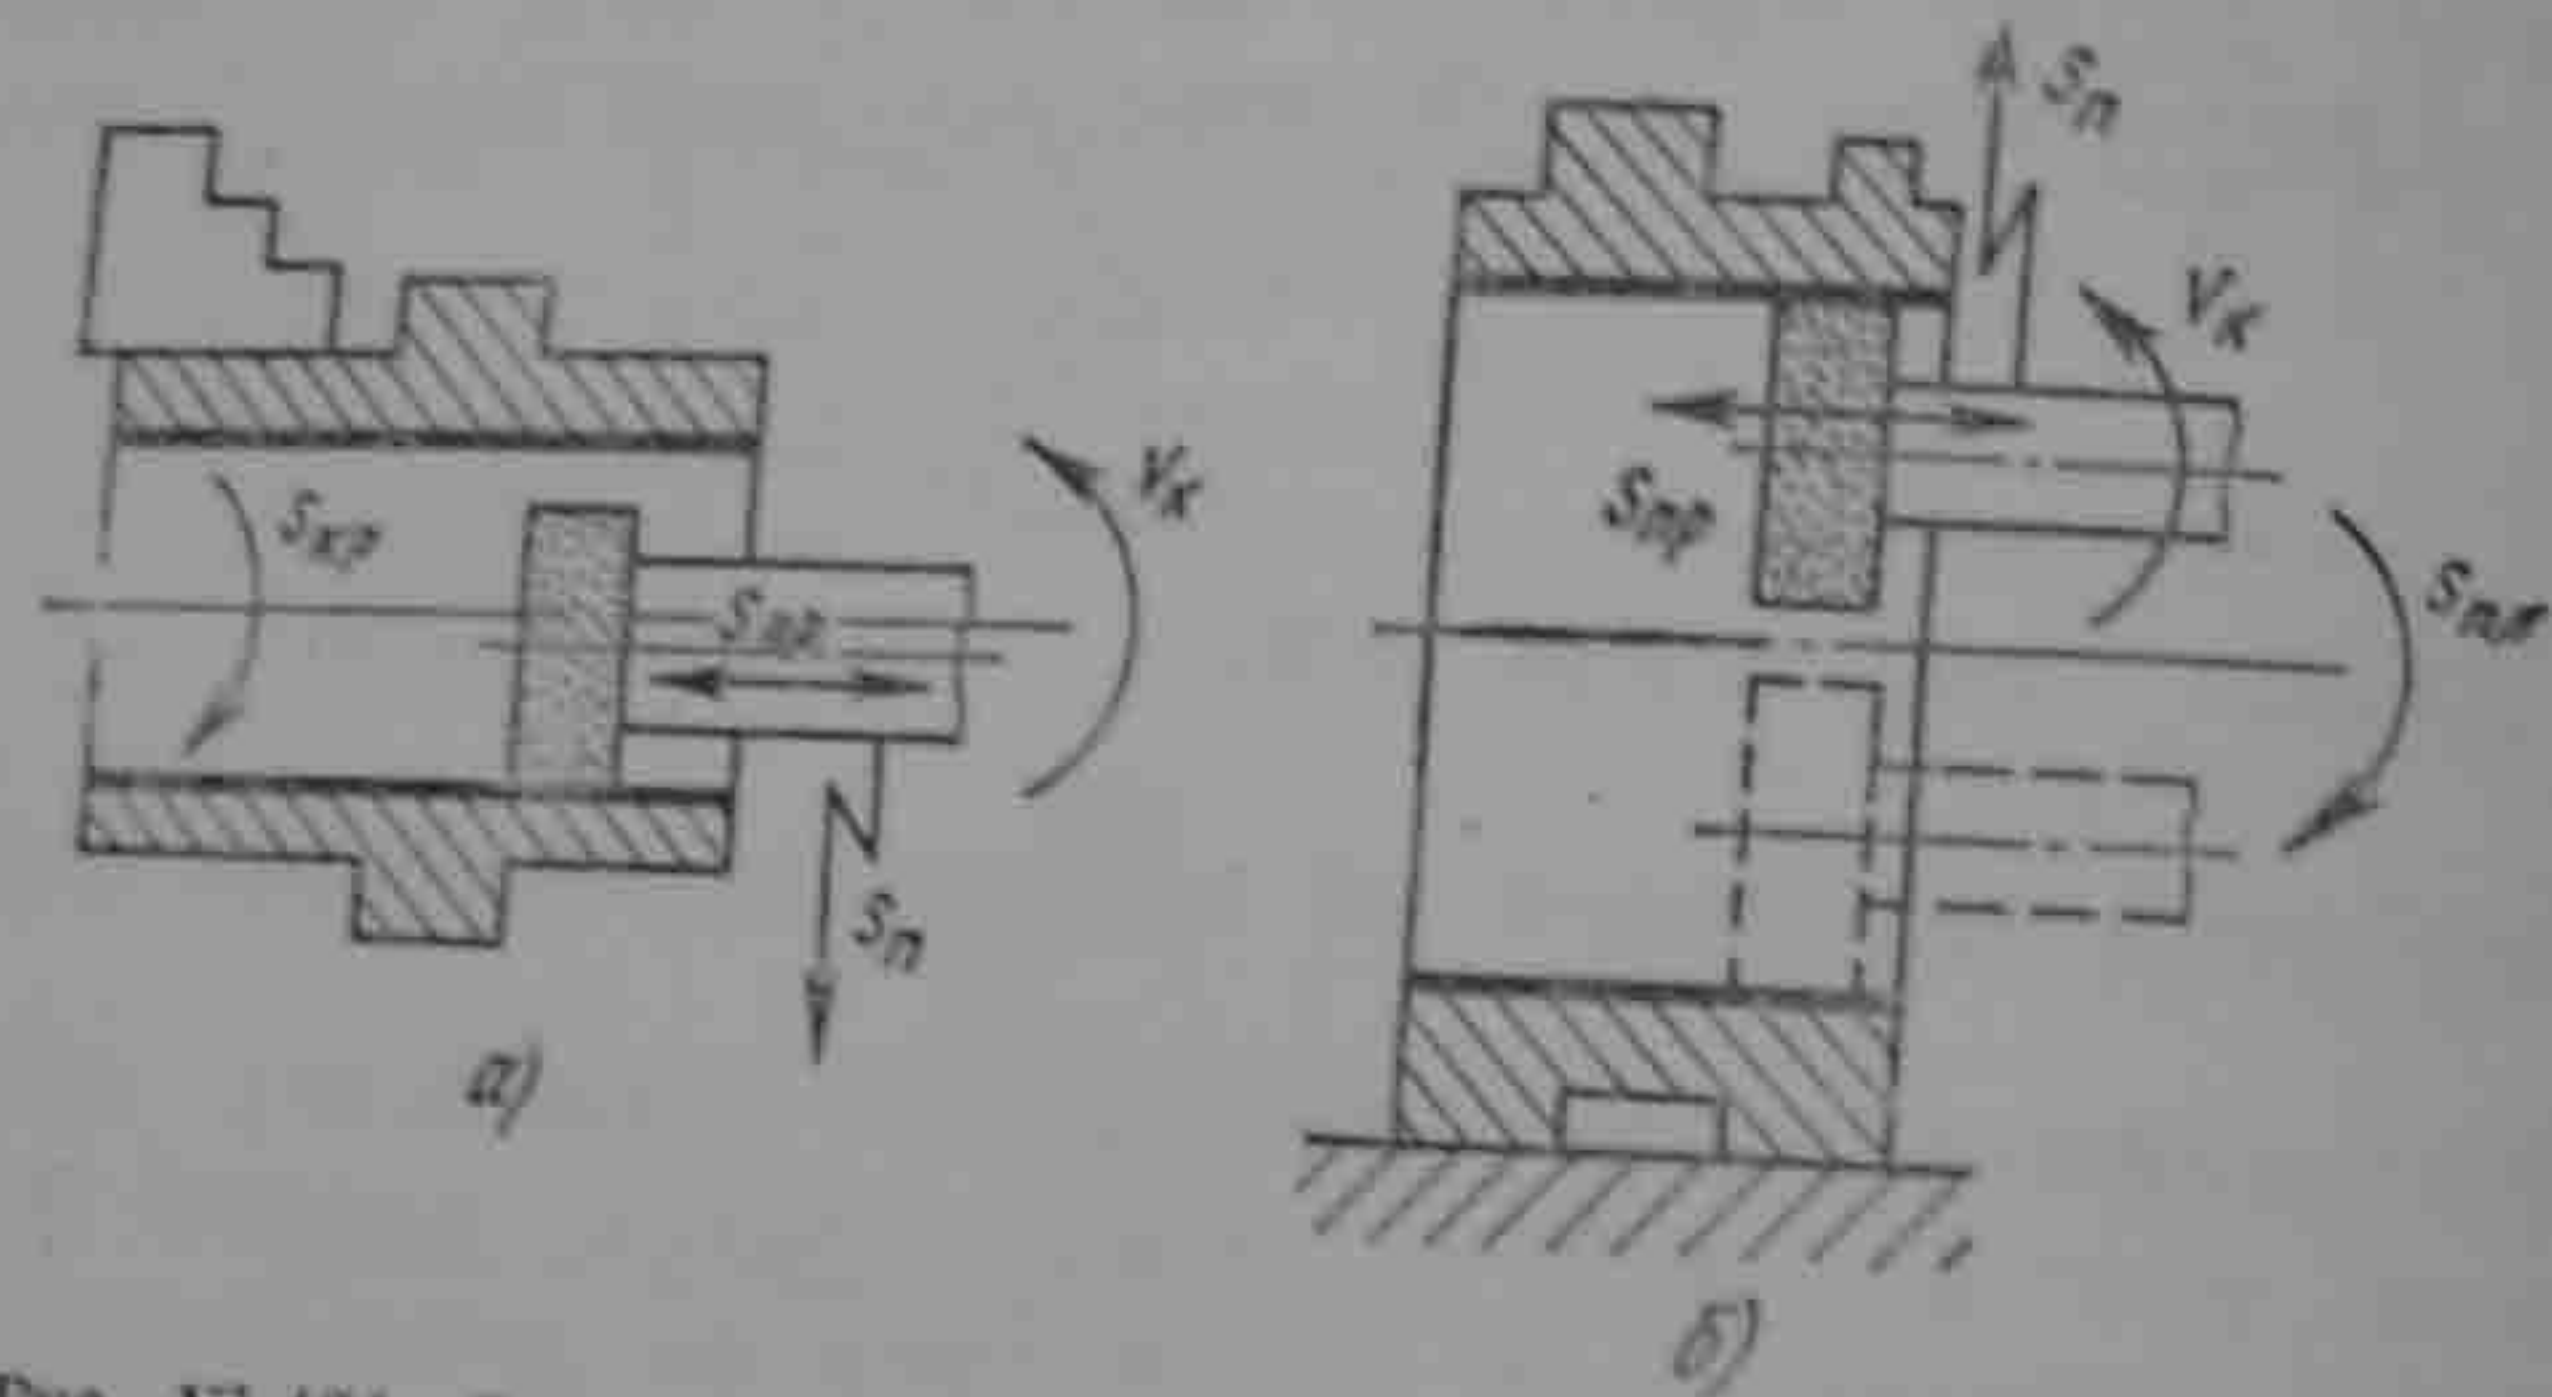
Схемы обработки заготовок на внутришлифовальных станках
